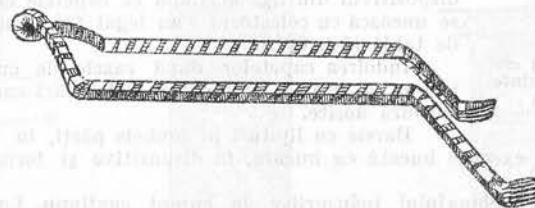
Bobinaj în bare, cu elemente având aceeași deschidere.
